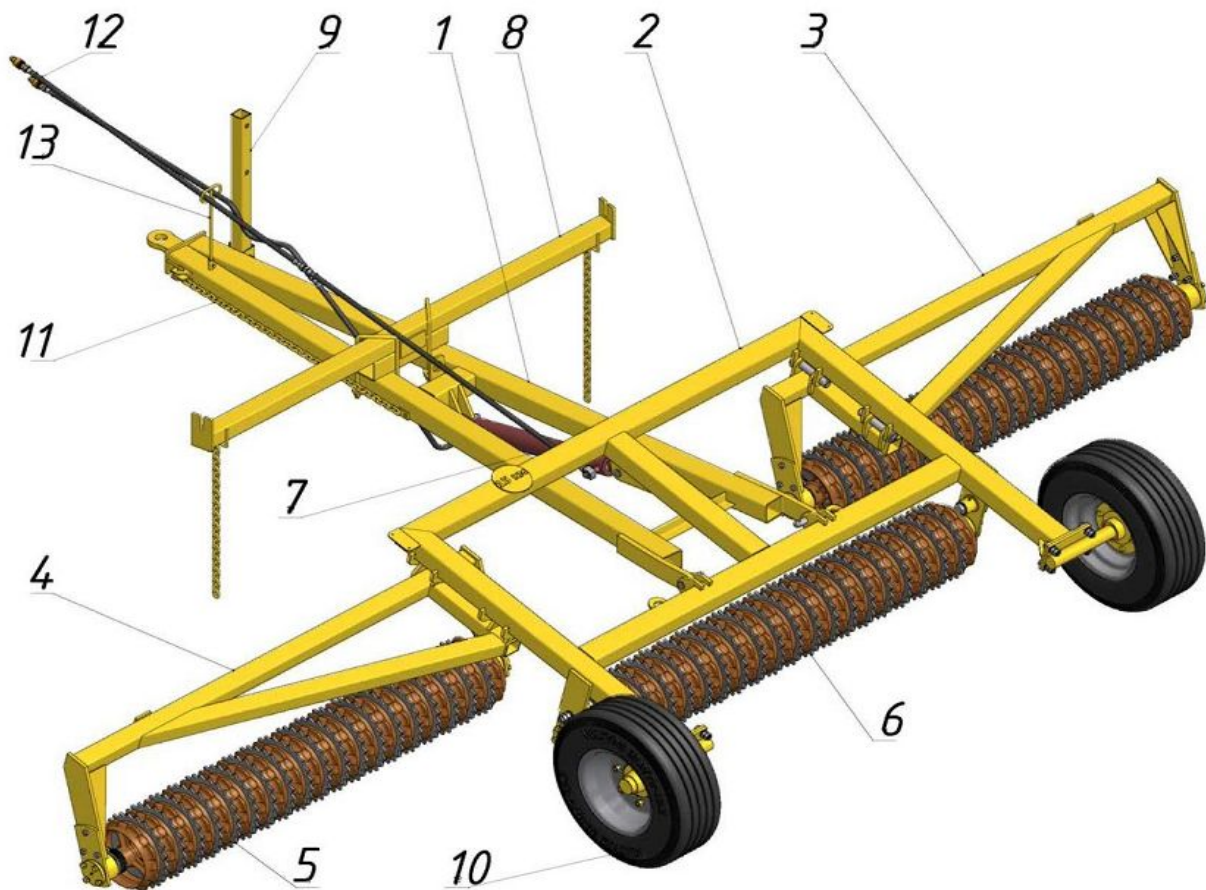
Каток кольчато-зубчатый ККЗ-6 в рабочем положении:
